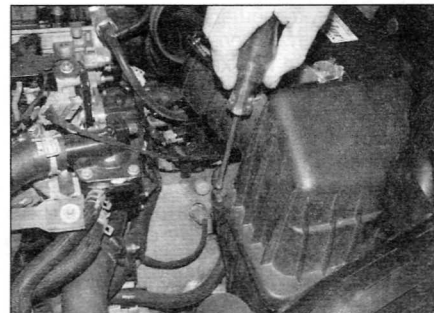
, а. Выверните два винта крепления крышки к корпусу воздушного фильтра...
